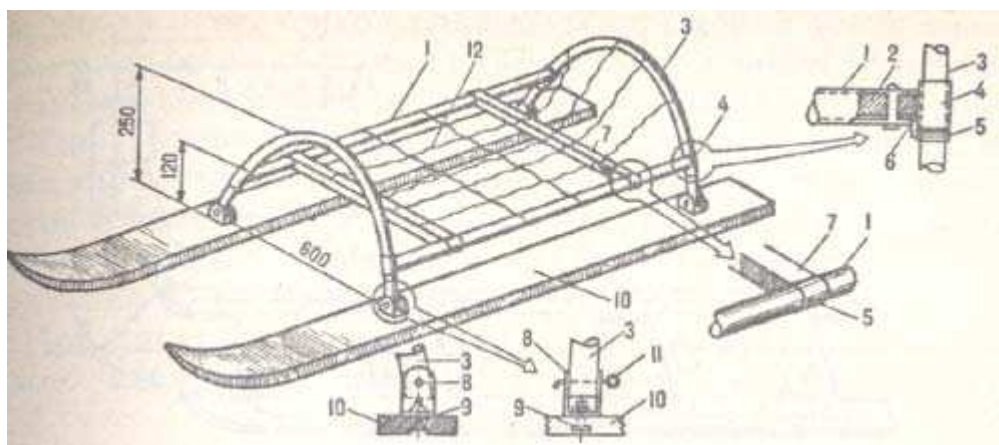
Индивидуальные нарты из лыж: 1 — продольная; 2 — деревянная пробка; 3 — дуга; 4 — амортизатор из микропористой резины; 5 — замотка киперной лентой; 6—фигурная скоба; 7 — поперечина; 8 — скоба крепления дуг к лыжам; 9 — болтики М-4; 10 — лыжи; 11—шпилька; 12 — оплетка.
